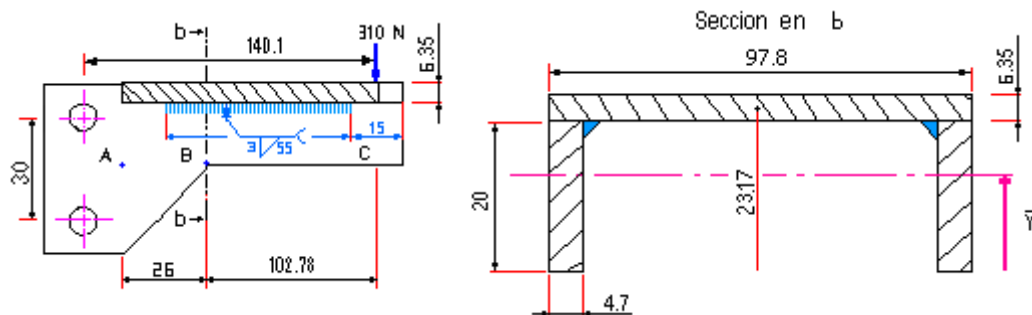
Esquema para el cálculo de la inercia del soporte de la carga (con corte que muestra la soldadura).
